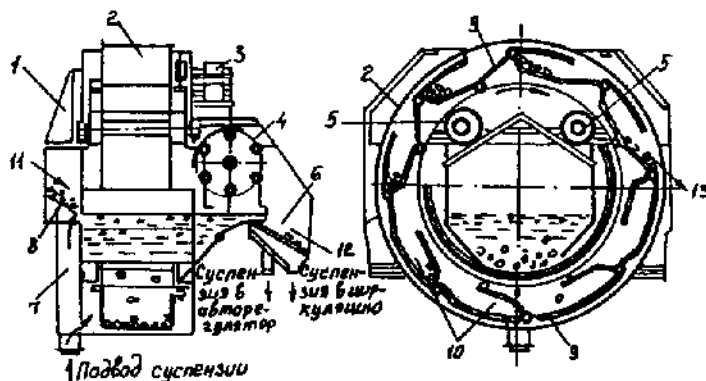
Тяжелосредный сепаратор с элеваторным колесом СКВ
